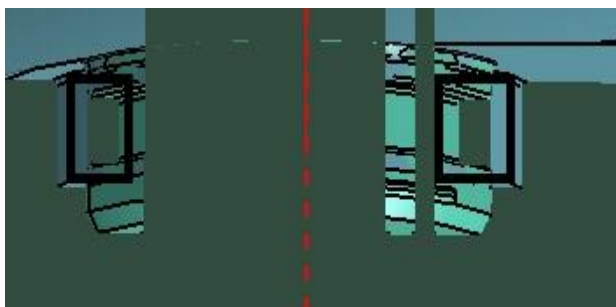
Výsledný inverzní objem spodní pracovní komory
